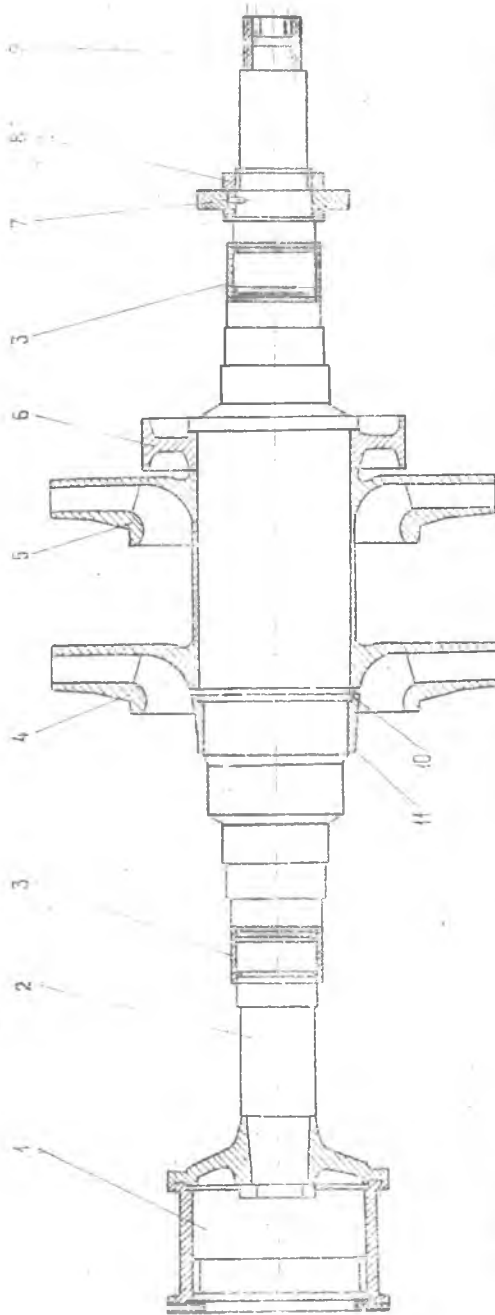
Ротор: 1 — муфта зубчатая; 2 — вал ступенчатый; 3 — гайка; 4, 5 — колесо рабочее; 6 — диск разгрузочный; 7 — диск упорный; 8 — гайка; 9 — муфта шлицевая; 10 — кольцо стопорное; 11 — штулка
